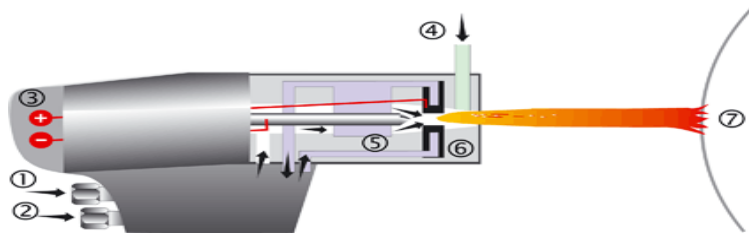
Плазмове напилення: 1 - захисний газ; 2 – вода для охолодження; 3 – трум; 4 – порошковий матеріал; 5 – катод; 6 – анод; 7 - деталь
